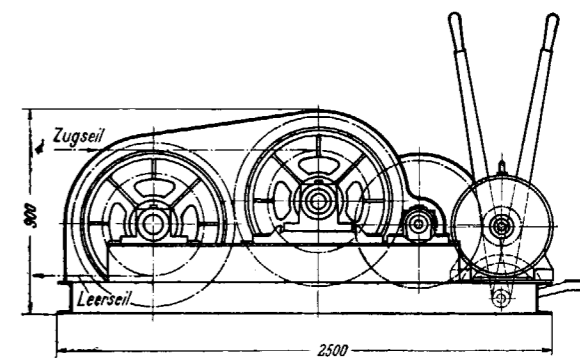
ª y 6.ª - Torno de la pala con tambores para el cable situados uno al lado del otro y provistos de frenos de cinta automáticos. a) tambores para el cable; b) engranaje; c) enganche suave; d) motor eléctrico; e) frenos de cinta; f) indicador de recorrido.
